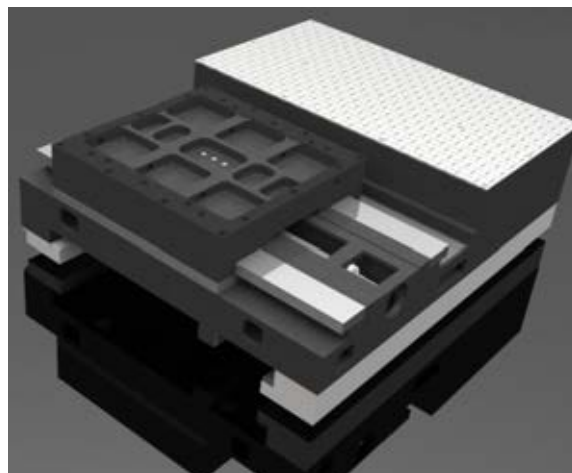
Общий вид суппорта тяжелого токарного станка 1К675.450Ф3
